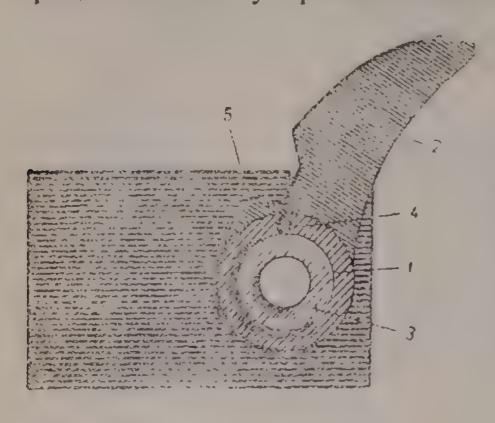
Правая задвижка: 1— ролик; 2— задержка; 3— шайба; 4— шплинг; 5— пятка
